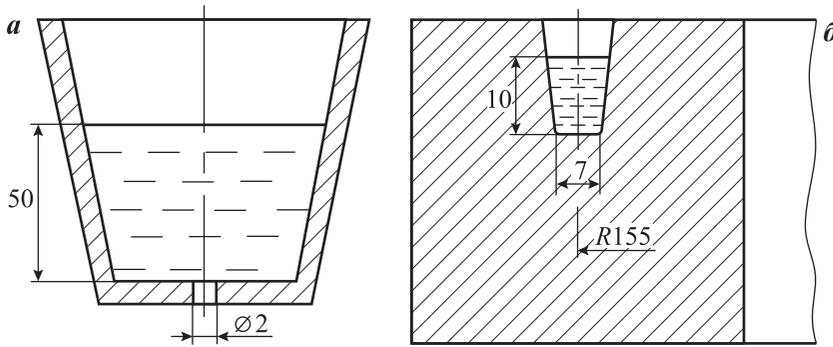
Дозатор (а) и колесо-кристаллизатор (б)
